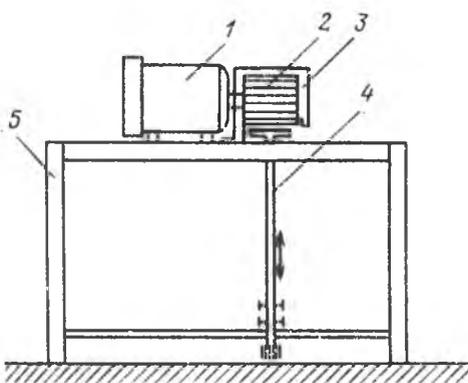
Монтажная схема устройства: 1 — электрический двигатель, 2 — фреза, 3 — защитный кожух, 4 — прижимной механизм, 5 — рабочий стол
